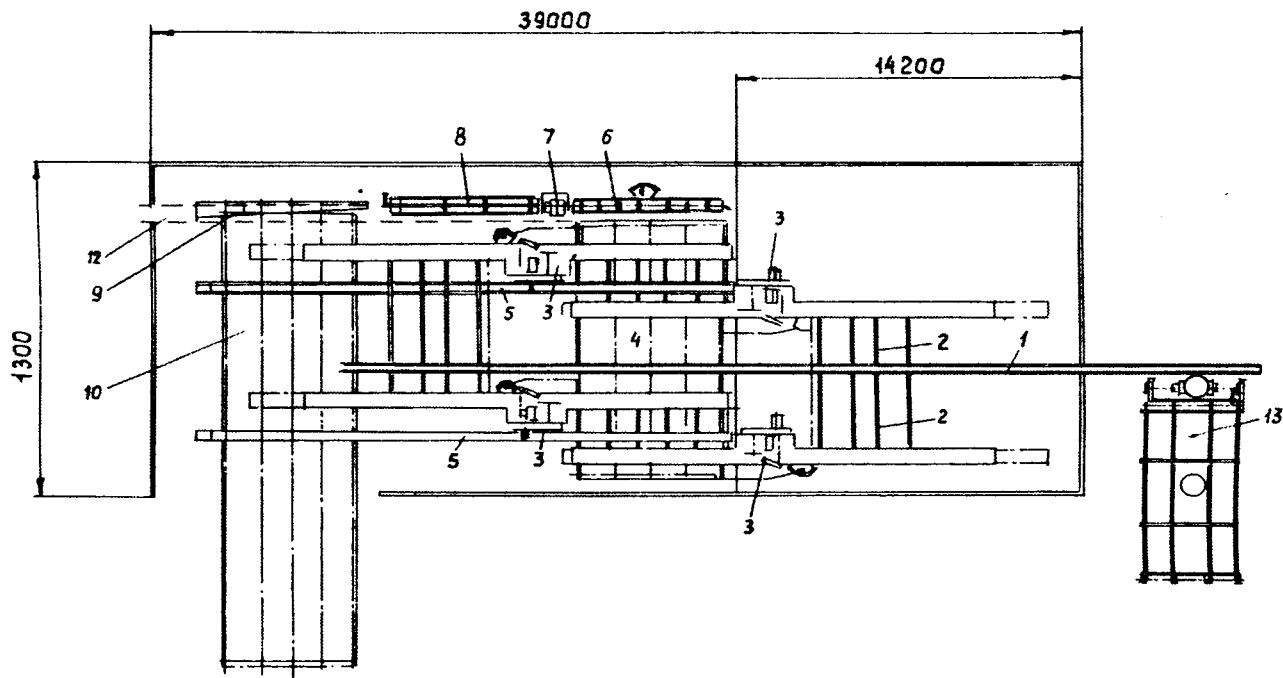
Схема лесопильного цеха с круглопильными станками Кара:
